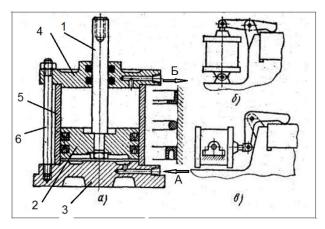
Пневмоцилиндры для станочных приспособлений: а – конструкция цилиндра; б – вертикальная установка цилиндра в приспособлении; в – горизонтальная установка в приспособлении
